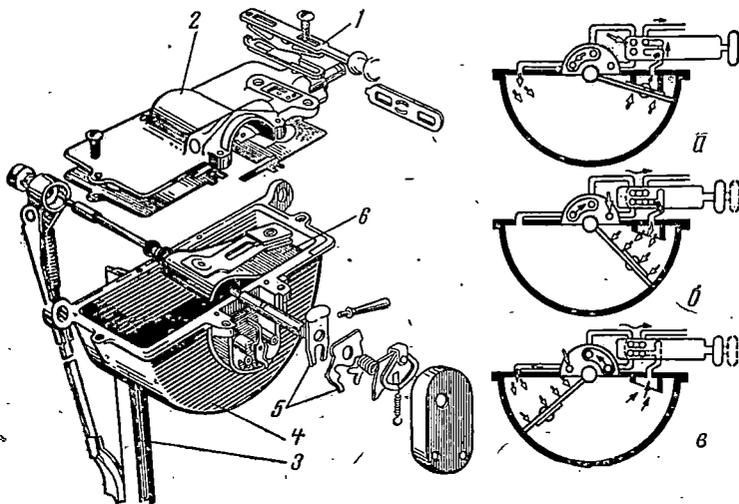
Стеклоочиститель автомобиля ГАЗ-51А:
